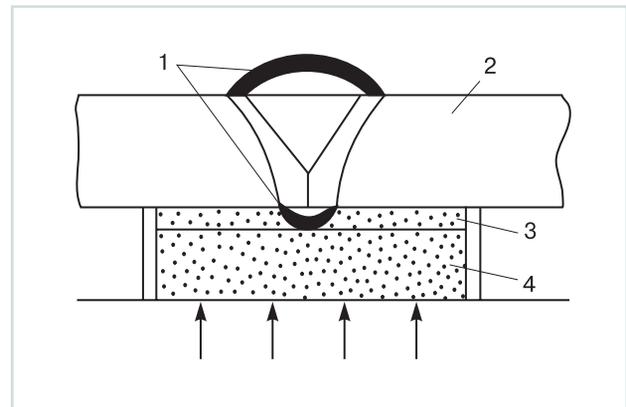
Схема односторонней сварки на двухслойной флюсовой подушке: 1 — усиление лицевой и обратной стороны шва; 2 — свариваемый металл; 3 — верхний, формирующий слой флюса; 4 — огнеупорный слой
